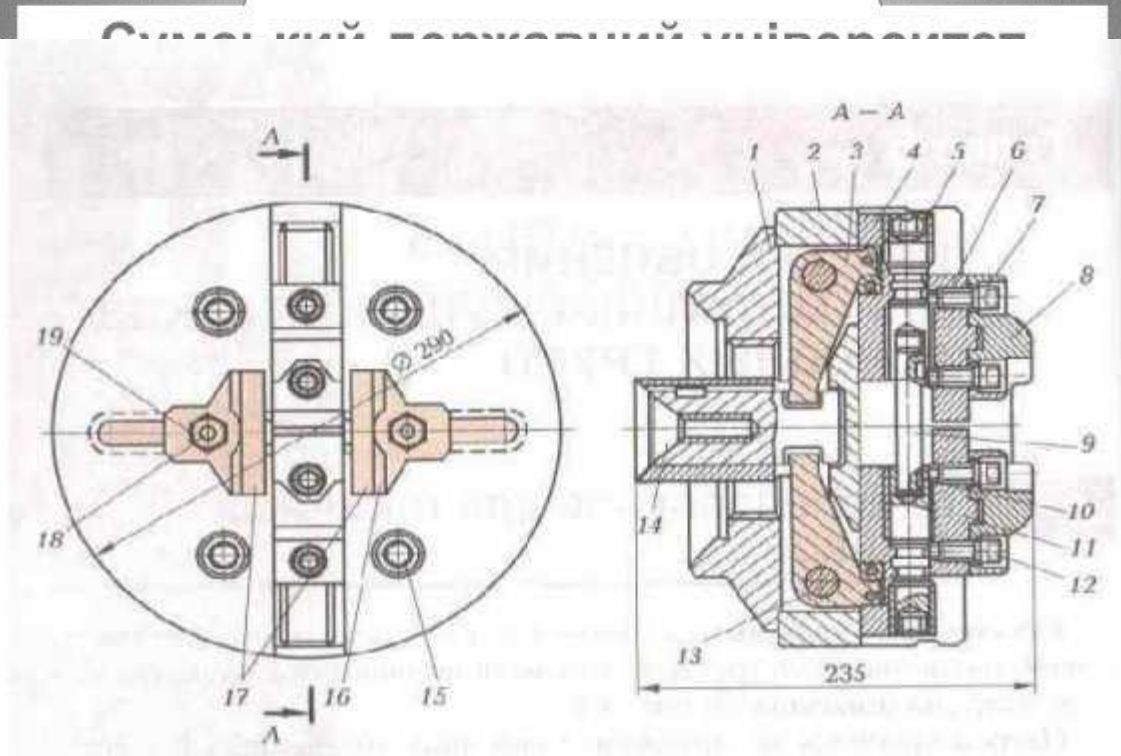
Конструкція автоматизованого двухкулачкового патрона:
